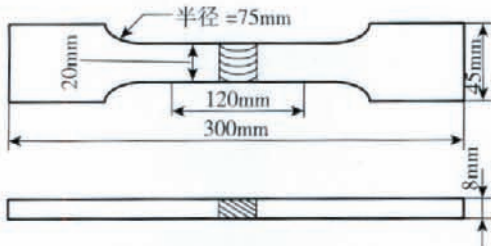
搅拌摩擦焊接头疲劳试件几何形状与尺寸
